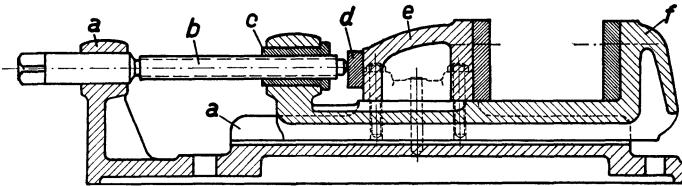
Unterzugschraubstock mit Gewindespindel, Schnitt.
